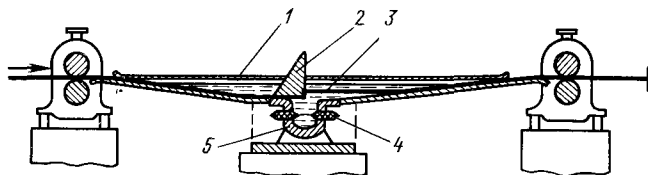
27 Электрогидравлическое устройство для резания непрерывно движущегося проката
